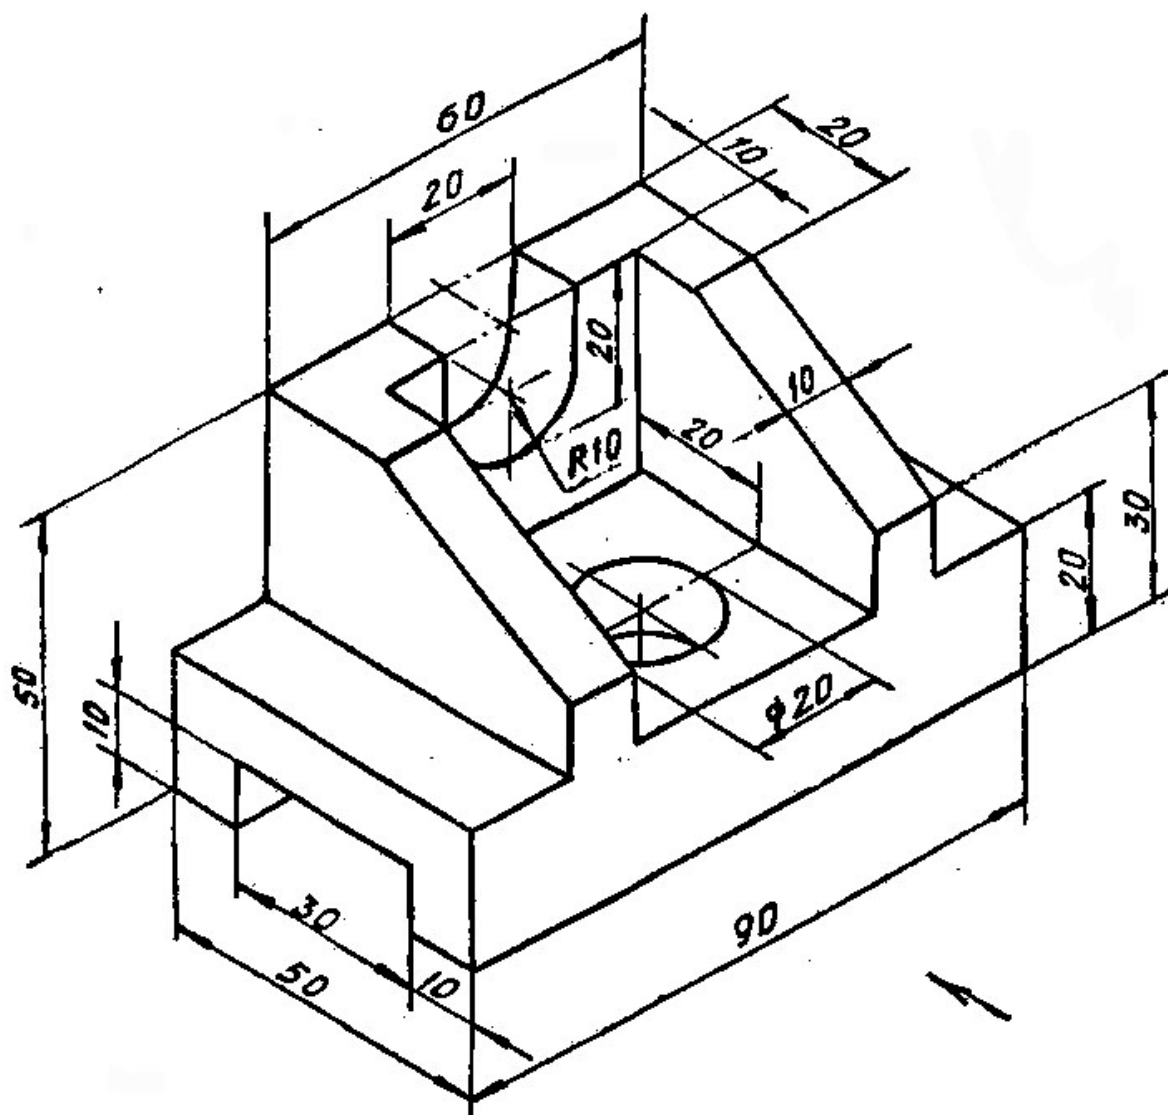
Деталь 5ти осевой обработки на станках с ЧПУ
